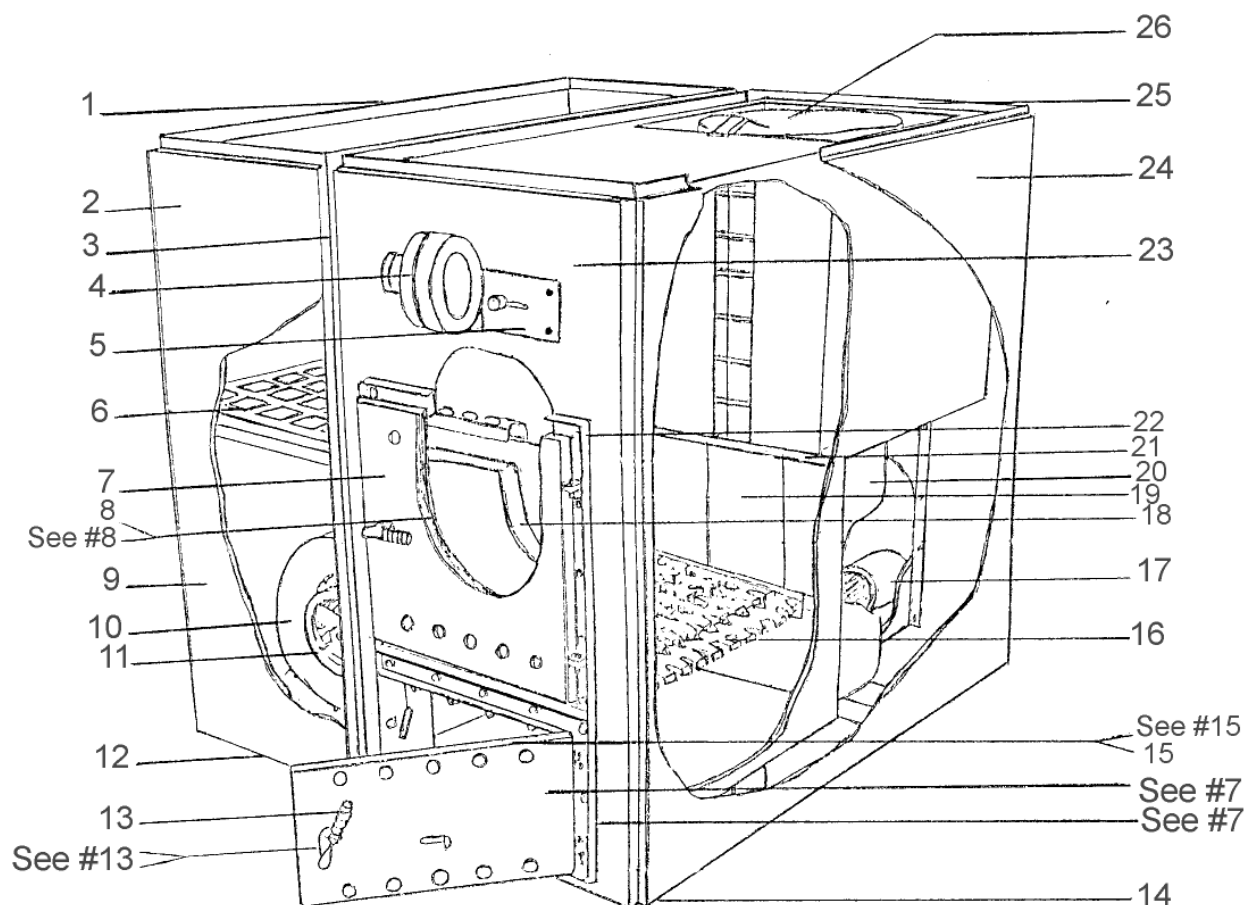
B - LISTE DES PIÈCES – CL115-170G
